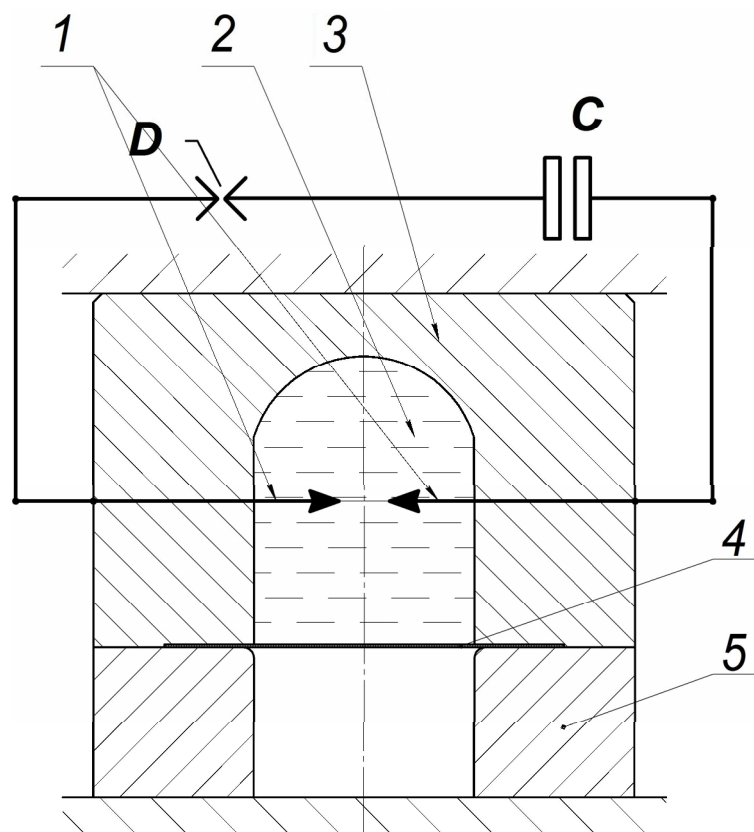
Схема ЭГИ вытяжки-формовки: 1 – электроды; 2 – рабочая жидкость; 3 – разрядная камера; 4 – листовая заготовка; 5 – матрица
